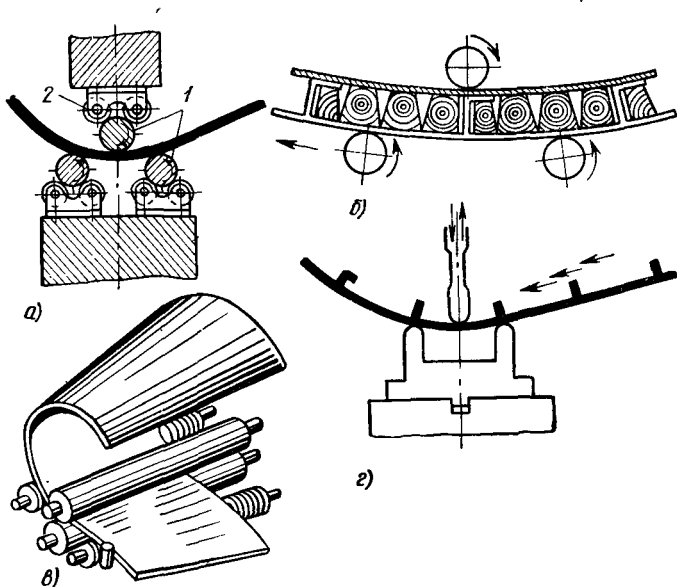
Схемы гибки на гибочно-листовых станках:
